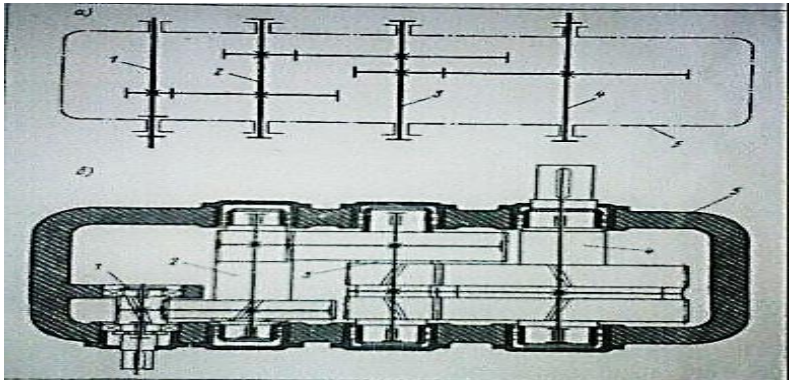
Редуктор зубчастий трьохступінчастий:
